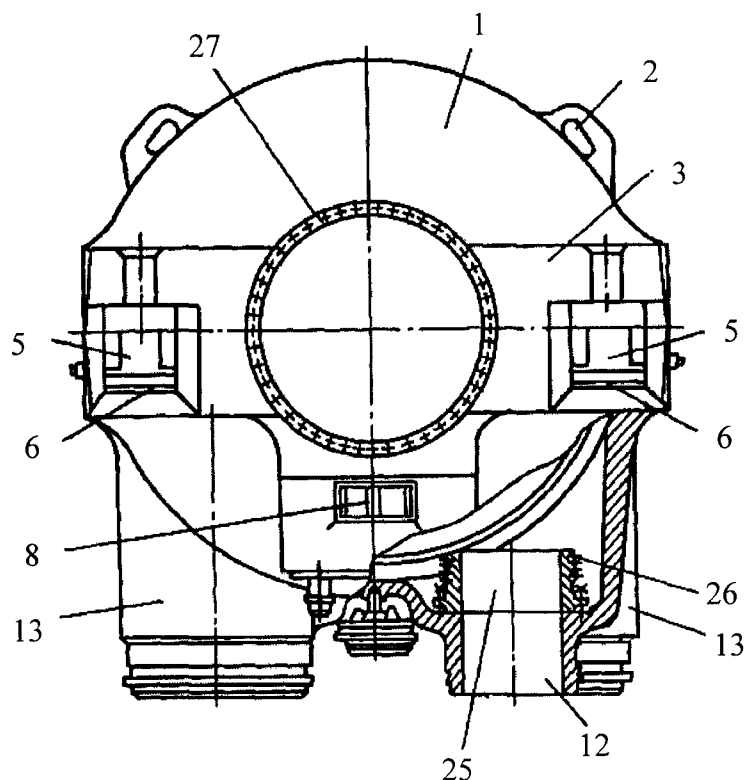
Внешний корпус ЦВД. Часть 1
